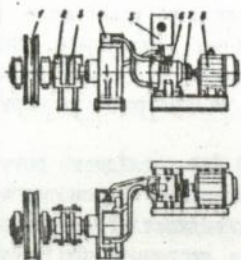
Механізм пересування мостового крану в/п 15/3т з роздільним приводом та високомомментними гідромоторами: 1-ходове колесо; 2-кожух; 3-муфта; 4-високомомментний гідромотор ТХХ; 5-поповнювальний бачок; 6-регулювальний вентиль ПД КБ; 7-муфта; 8-приводний електродвигун
